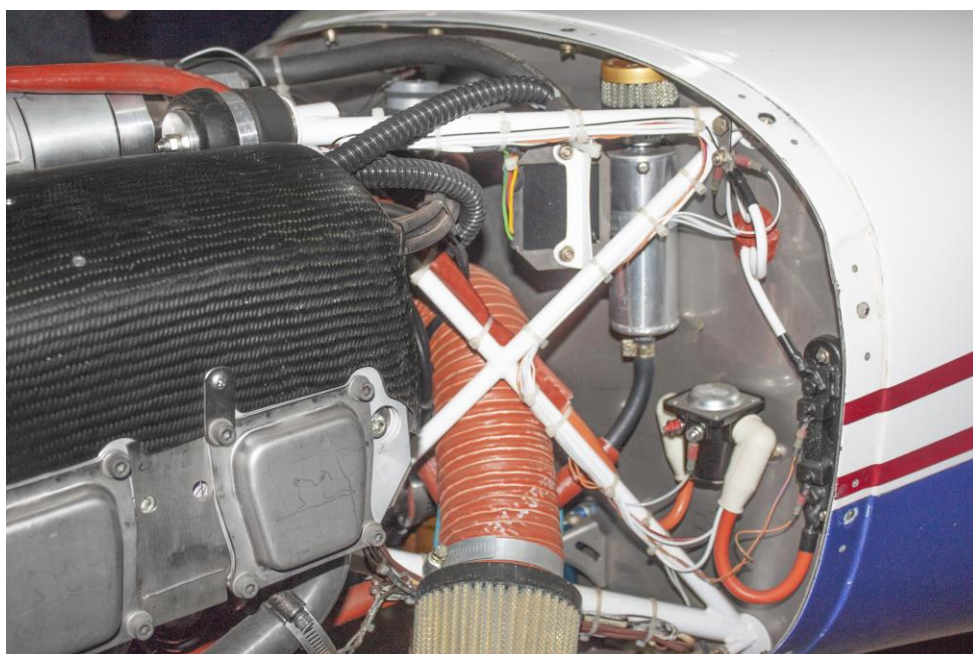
Berço do motor Jabiru 3300 fixado
